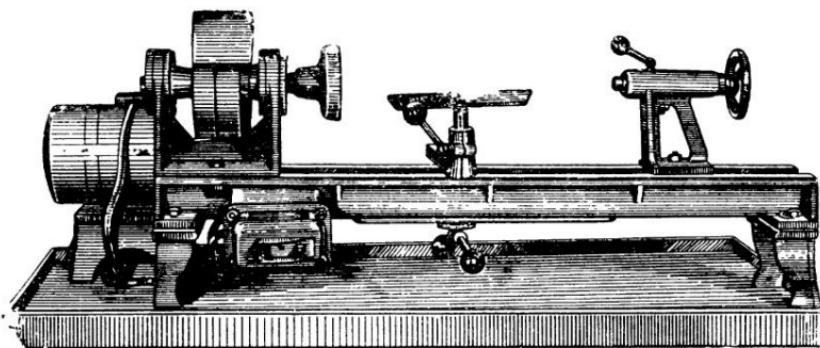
Токарные станки: вверху — токарный станок ТД-120;
